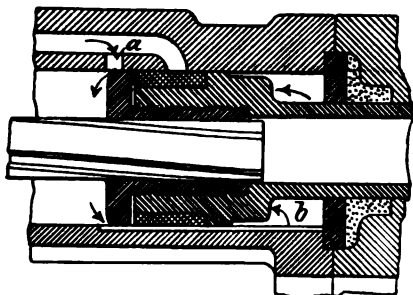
Hubbegrenzung der Bohrmaschine von Bechem & Keetmann.
